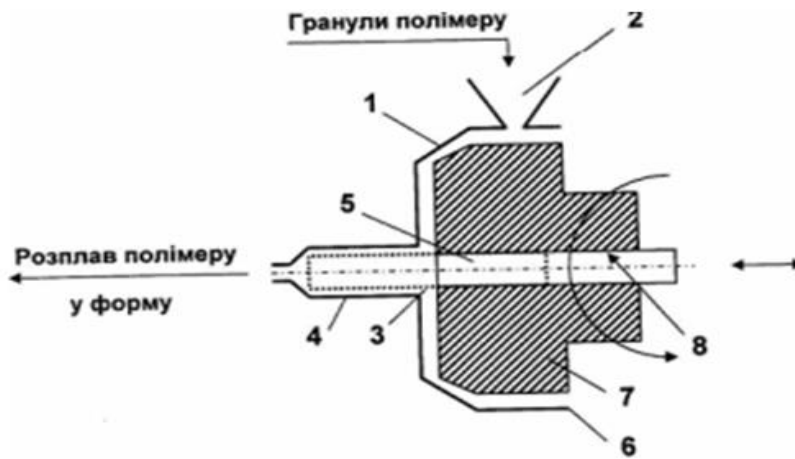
Конструкція корпусу інжекційного вузла
